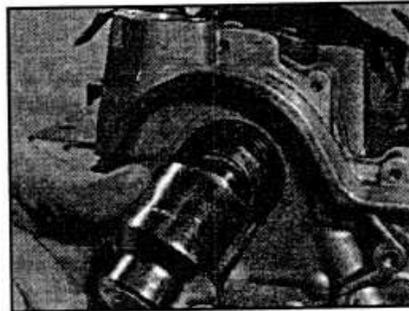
С.58. Использование оправки для установки уплотнительного кольца коленчатого вала.
